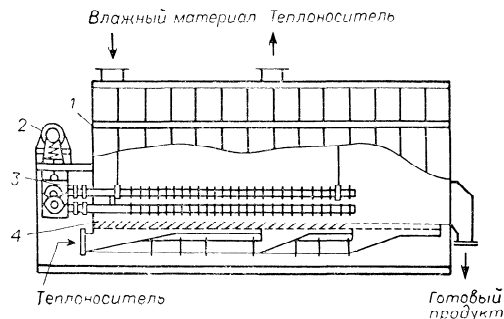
Сушилка кипящего слоя с вибрирующими поверхностями нагрева (конструкция ВНИИХИММАШа):
